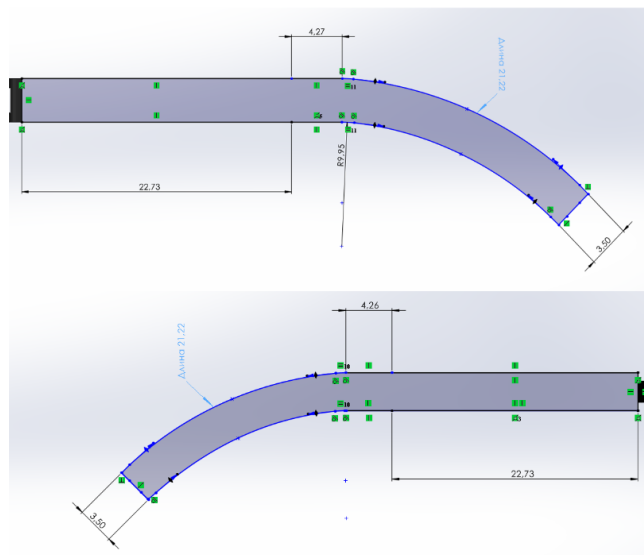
Ескіз робочої частини інструменту в середовищі Solidworks
